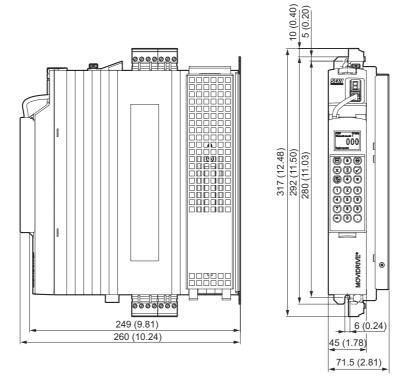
Dimensões MDX60B, tamanho 0S com resistência de frenagem, em mm (in)
